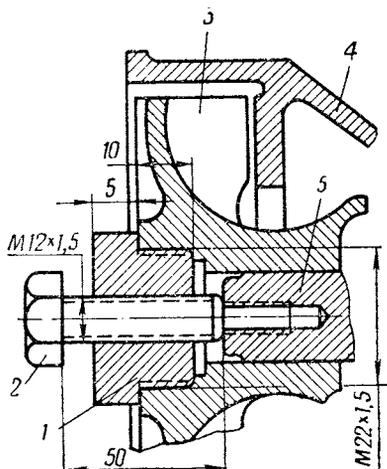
Установка съемника для спрессовки крыльчатки водяного насоса:
